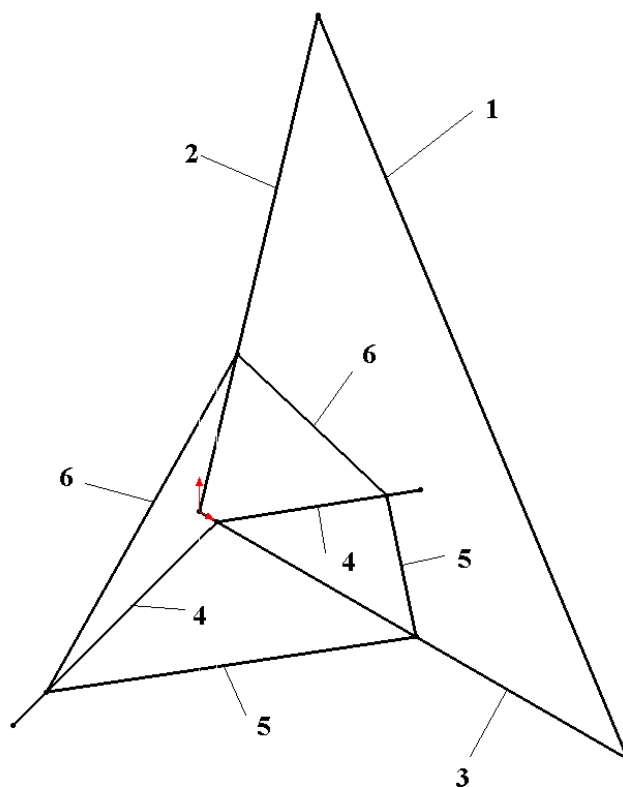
Bokocrt rešetkaste konstrukcije jedrilice
